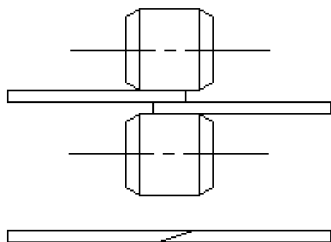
(a) - Soldagem por Costura com Deformação Plástica.
